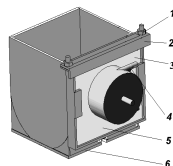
Конструкция рабочей камеры для ВиАУЗО деталей в свободном состоянии с расположением ультразвукового преобразователя в стенке рабочей камеры: 1 – резьбовые соединения; 2 – крепление; 3 – смотровой люк; 4 – штуцер для подачи охлаждающей жидкости; 5 – ультразвуковой преобразователь; 6 – рабочая камера
